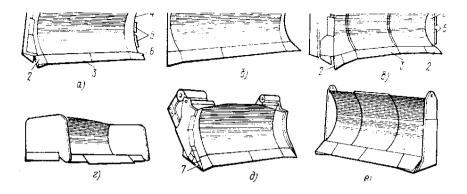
Основные типы отвалов бульдозера: а – прямой; б – универсальный (поворотный); в – сферический; г – совковообразный; д – с боковыми рыхлящими зубьями; е – короткий толкающий; 1 – лобовой лист; 2 – угловые ножи; 3 – средние ножи; 4 – боковые щитки; 5 – боковые ножи; 6 – открылки; 7 – выдвижные зубья
